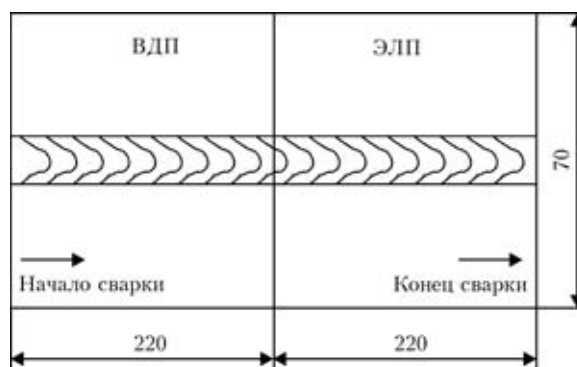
Схема сварки образцов способами АДС, АДС по флюсу и ЭЛС
